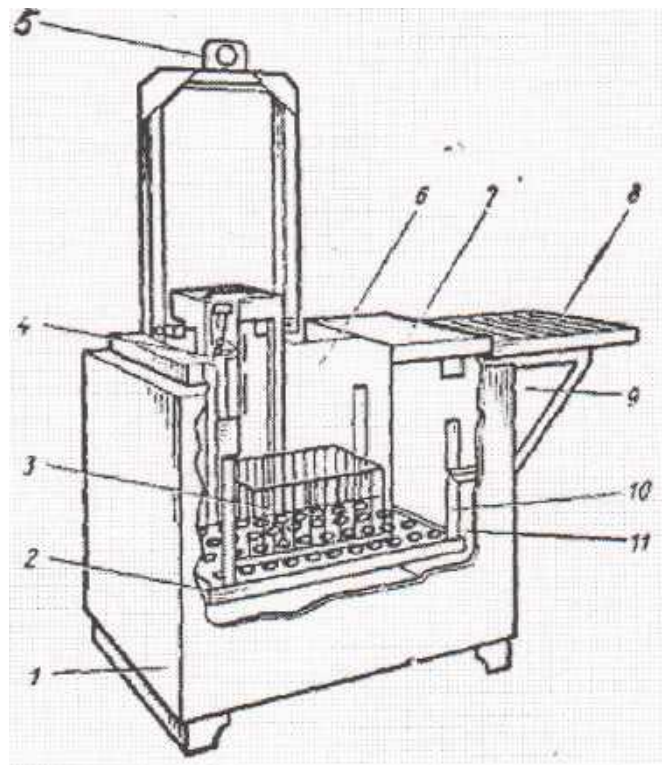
Ванна з платформою, що коливається: 1 – корпус;
